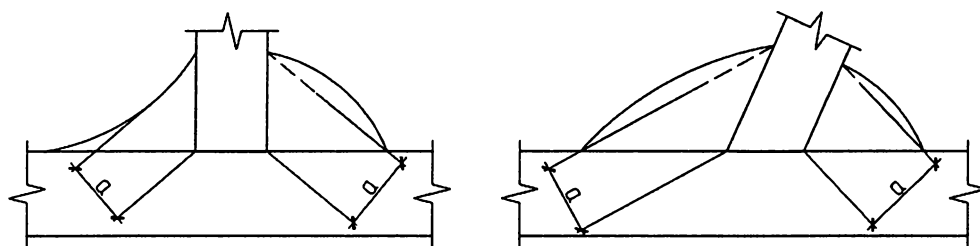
(рис. 4.3 [28]) – Эффективная толщина углового сварного шва
